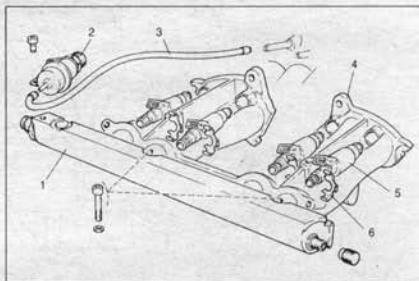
Снятие топливной рампы с форсунками: 1 - рампа форсунок; 2 - регулятор давления; 3 - вакуумный шланг; 4 - впускная труба; 5 - форсунка; 6 - защелка форсунки
